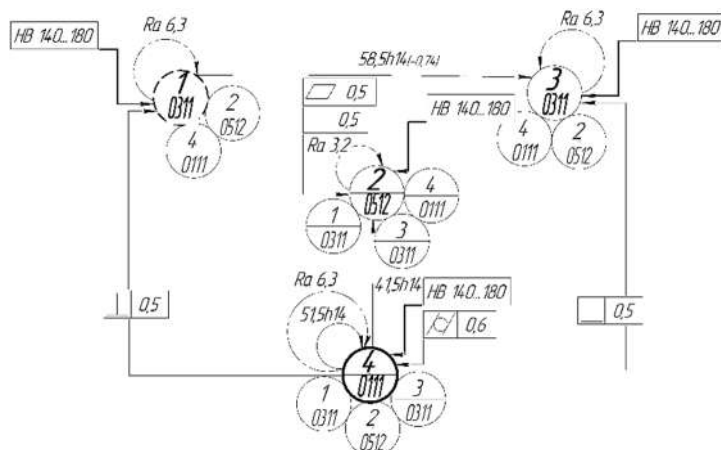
Граф размерных связей между элементарными поверхностями заготовки детали «Валик» (штамповка)
